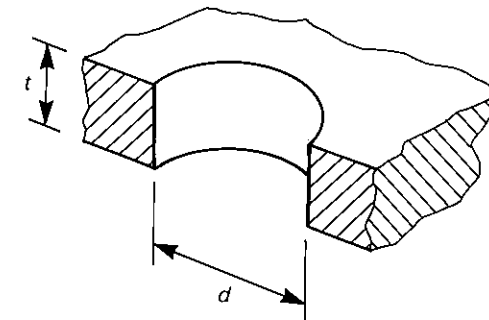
Bohrungen in den Scheiben sorgen nicht nur für geringeres Gewicht. Sie verändern, abhängig von den Abmessungen der Bohrungsdurchmesser d und der Scheibendicke t , auch die Oberfläche.
